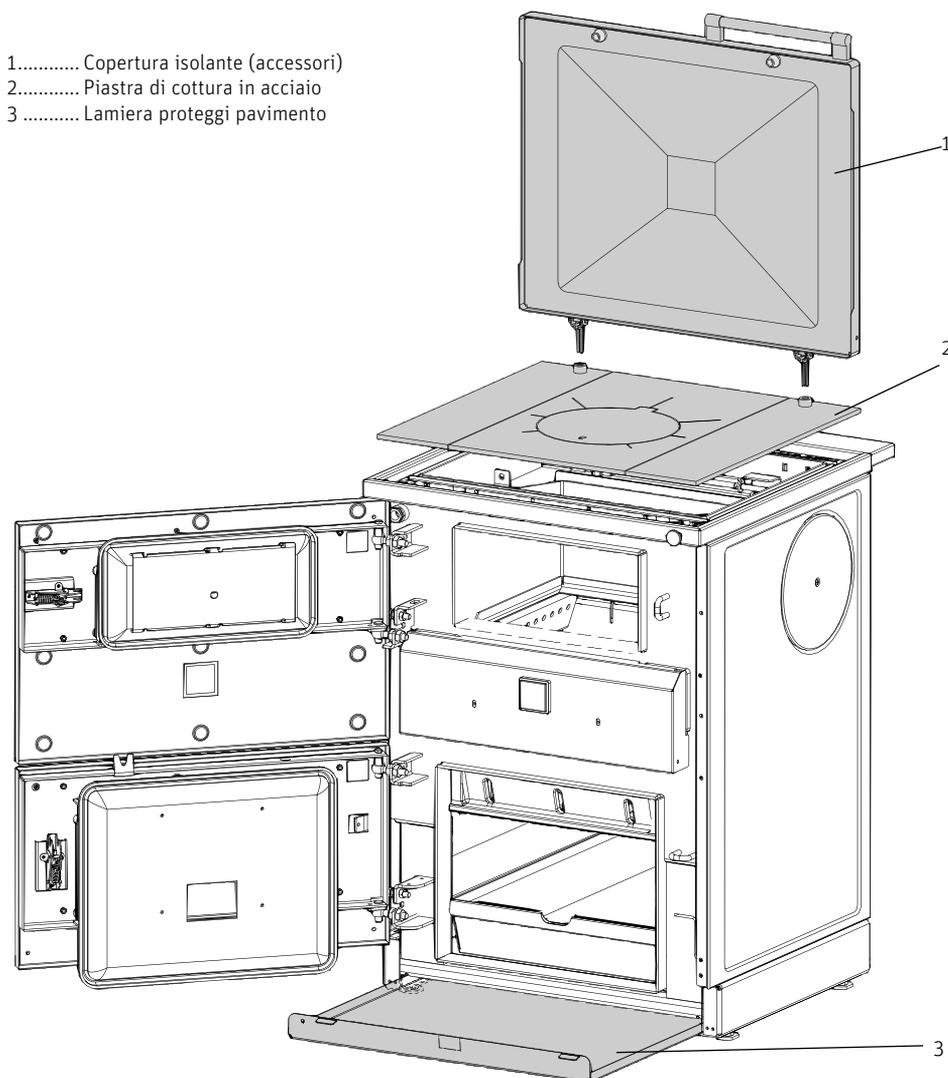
Montare piastra/piastre di cottura in acciaio, copertura isolante (accessori) e lamiera proteggi pavimento
